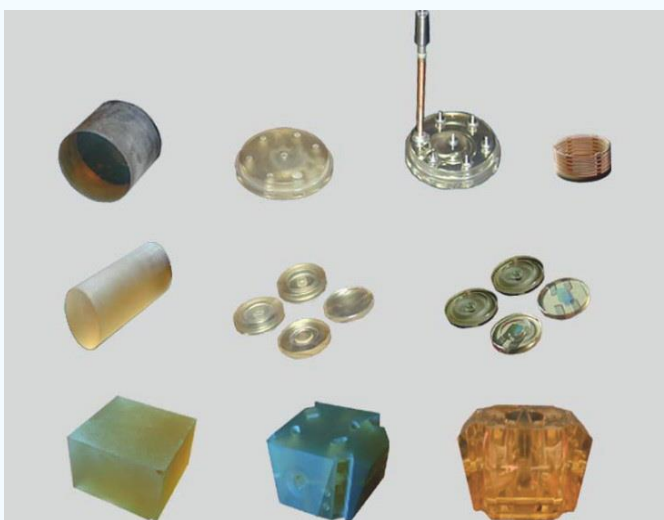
а) Заготовки и детали из ситалла для резонатора
